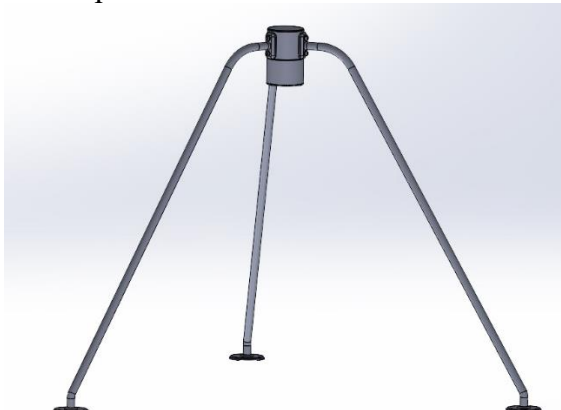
Вариант конструкции крепления ПНП для установки на площадке
